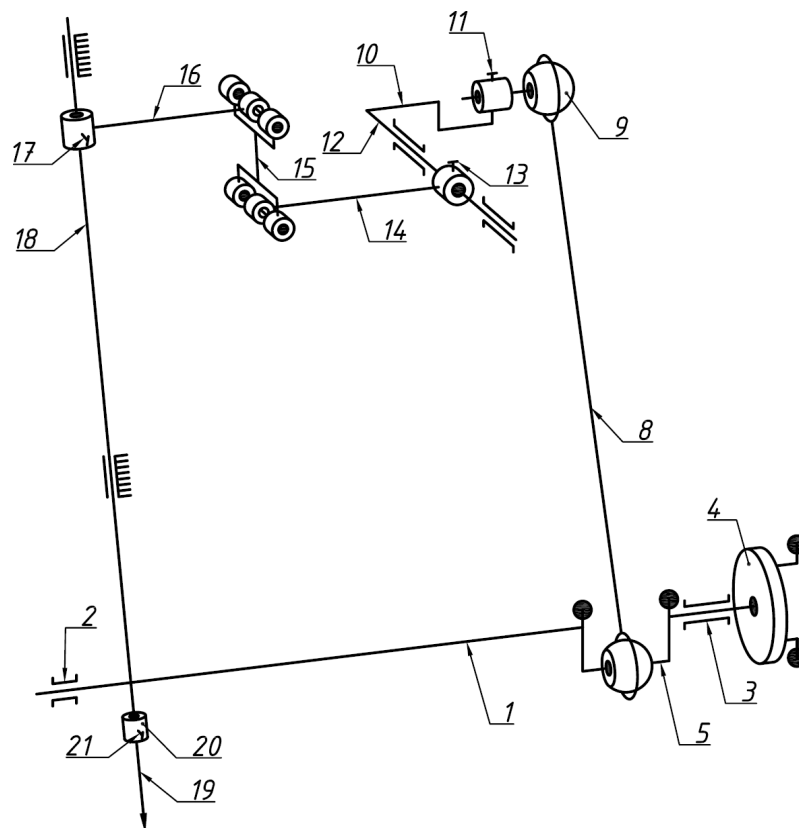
Схема механізму голки швейної машини 51 кл.
